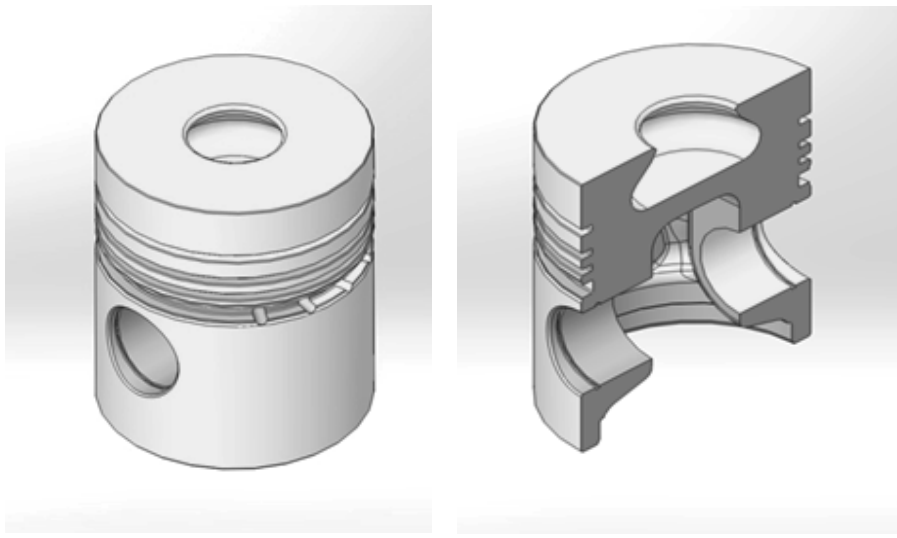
3D-модель литой детали поршня Д 240-1004021
